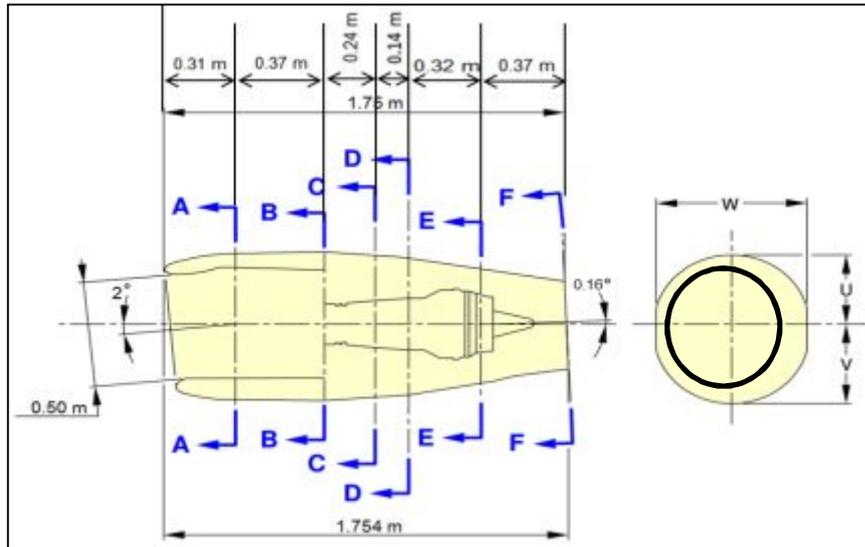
Dimensiones motor IAE V2500 a escala 1:3
